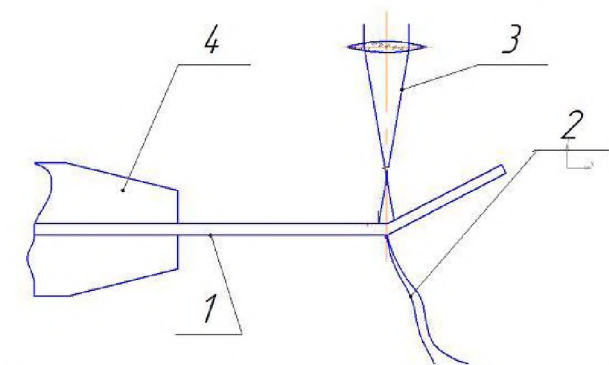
Схеми вимірювання температури зразка під час обробки: 1-зразок, 2-термопара, 3- лазерний промінь, 4-фіксатор.
